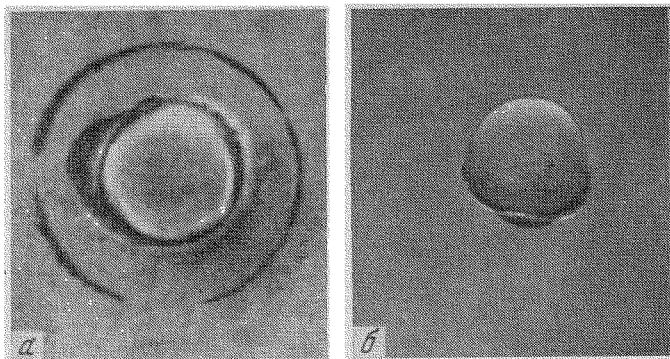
Отпечатки сварочных наконечников на детали
